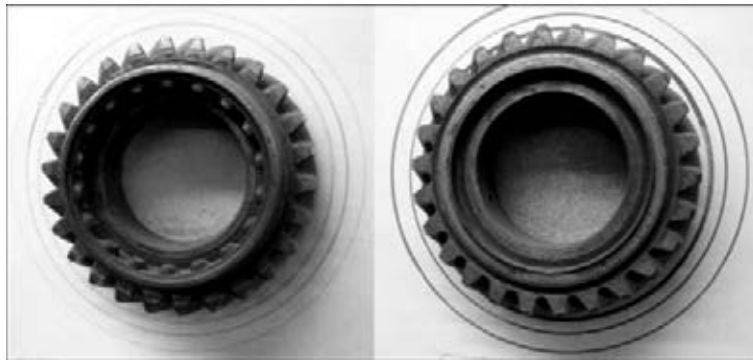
Лазерная сварка шестерен коробки передач
